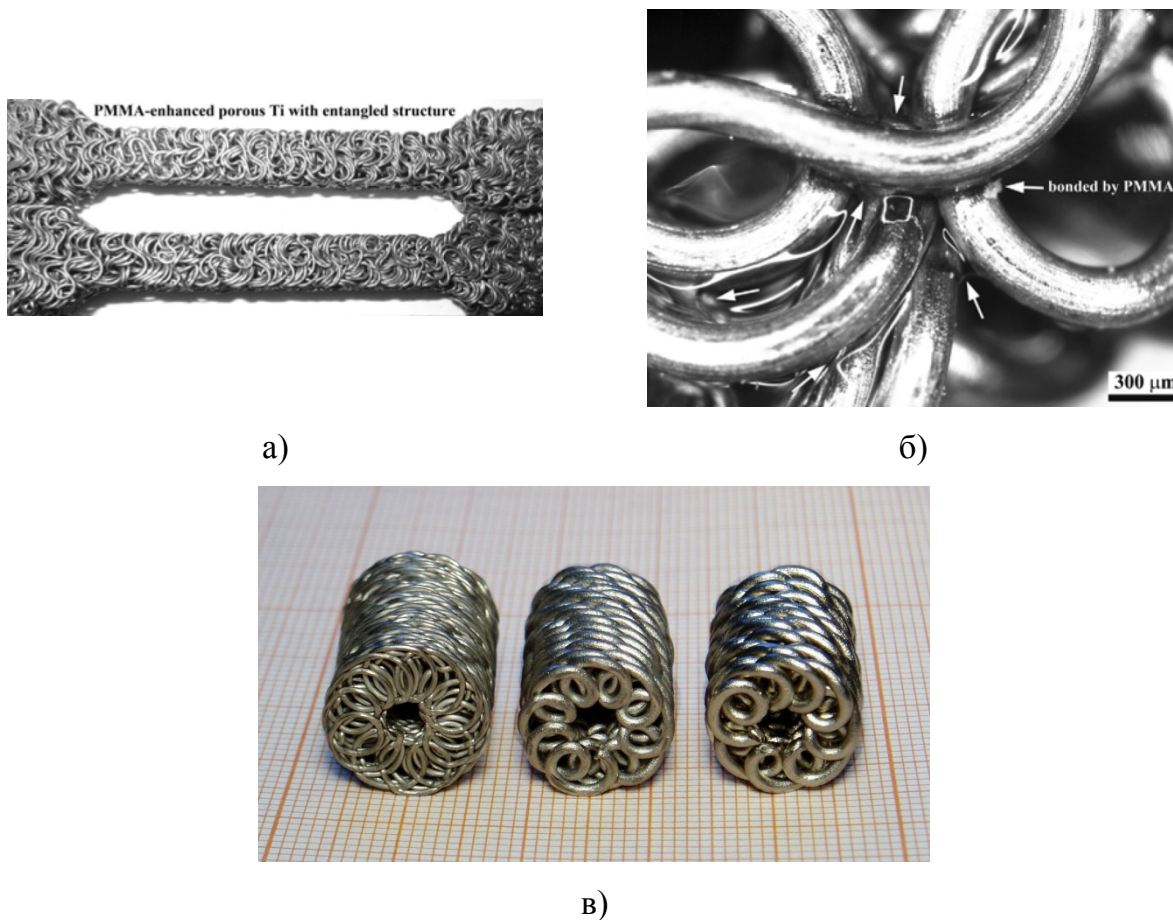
Внешний вид проволочных образцов: а, б – из «путанки» титановой проволоки, скрепленной полиметилметакрилатом (PMMA) [39]; в – из спиралей, скрепленных диффузионной сваркой [34].
